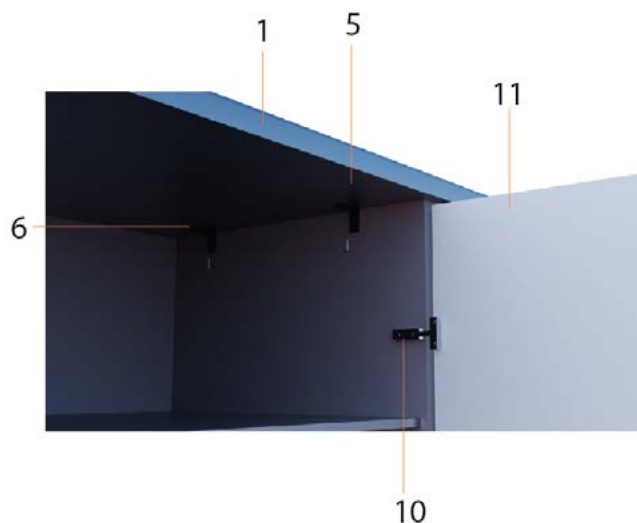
Detalle constructivo 3d mueble de cocina con mesón de acero inoxidable
